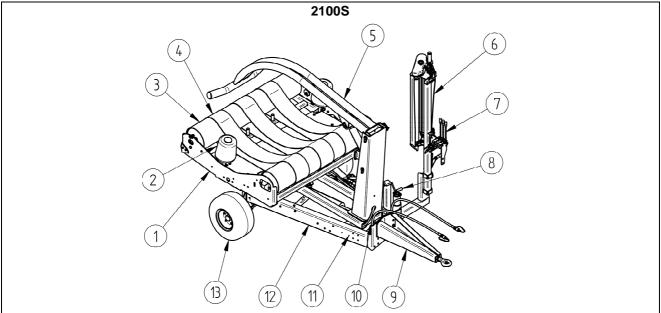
Vue d'ensemble de la machine avec ses principaux groupes
